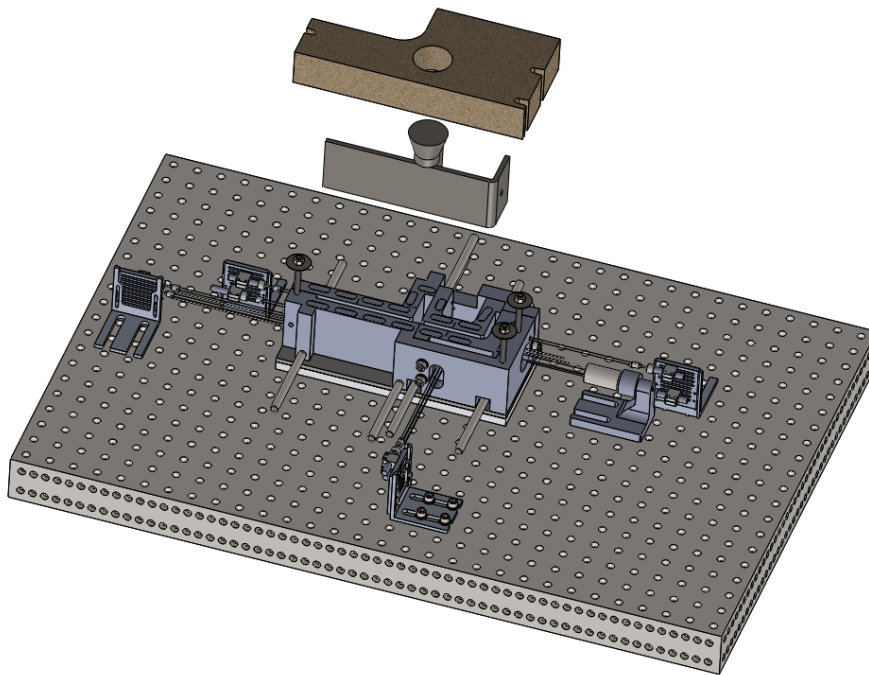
Versuchsaufbau für das Bauteil mit komplexer Geometrie
